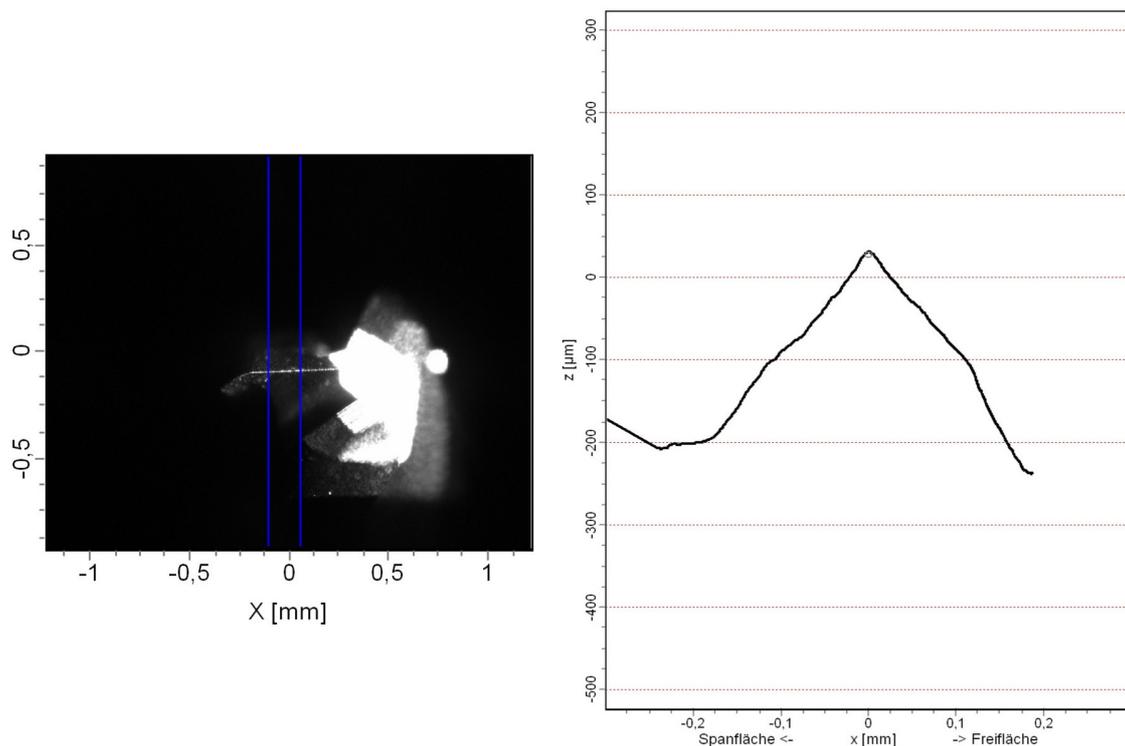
Fräser $D=0.5\text{mm}$, Werkzeugspitze verrundet mit 4my , Foto mit Messbereich sowie zugehörige Schnittdarstellung
